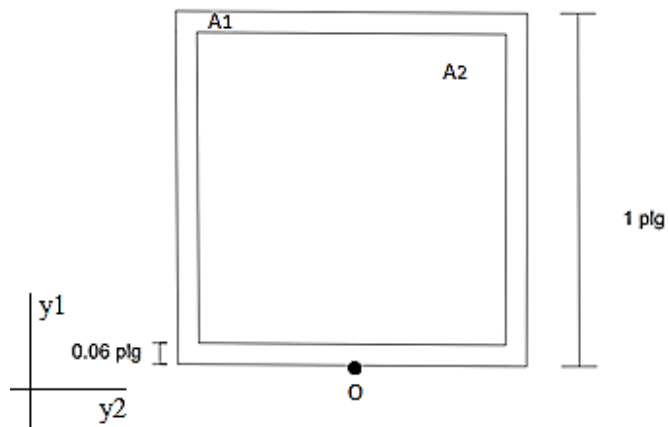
Geometría del material propuesto para la estructura del sistema de elevación.
